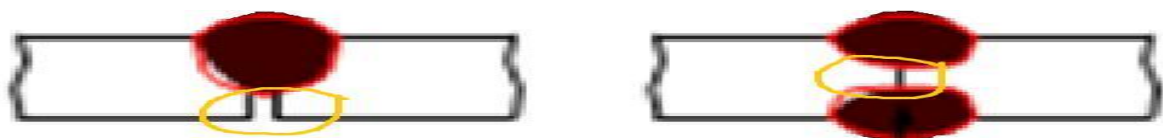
Soudure ou un excès dans la passe précédente.
